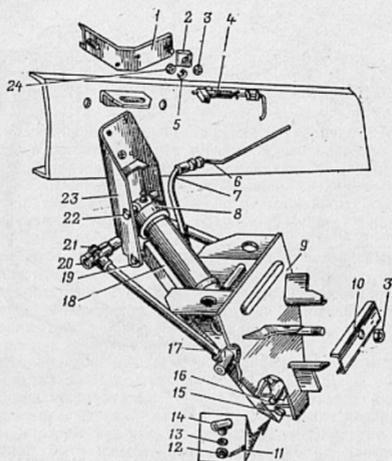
Горизонтальный держатель запасного колеса шасси Урал-375Е:
